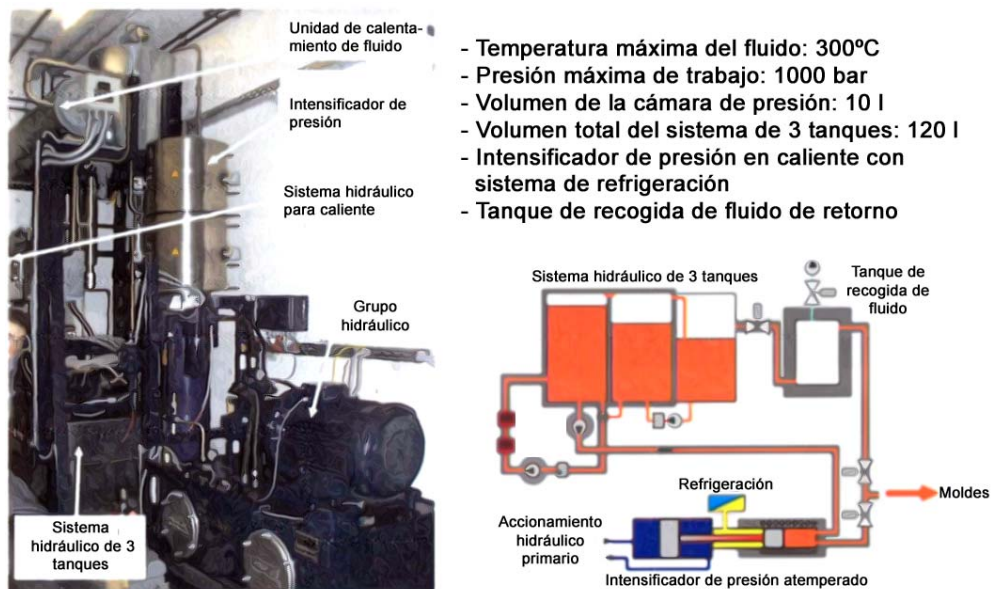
Instalación piloto para WHF desarrollado por la universidad de Erlangen (Geiger, et al., 2003)
